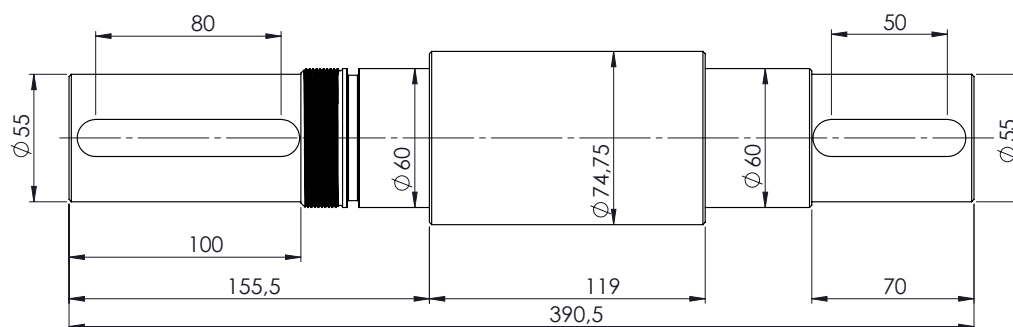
„Ableitungszeichnung“ Antriebswelle- Motor
